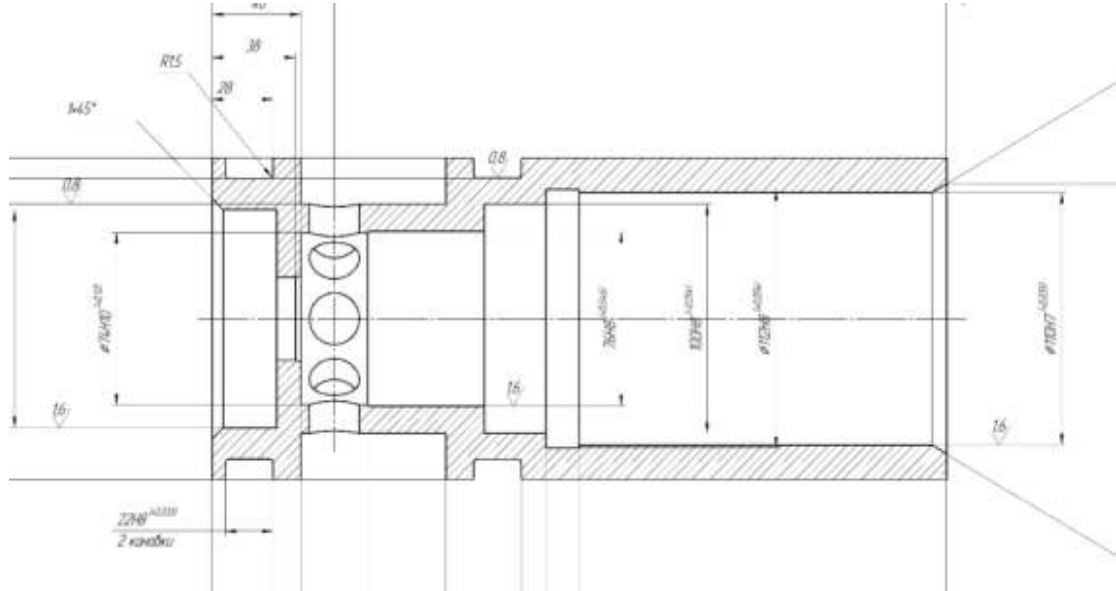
Фрагмент кресленника деталі «Гільза»
